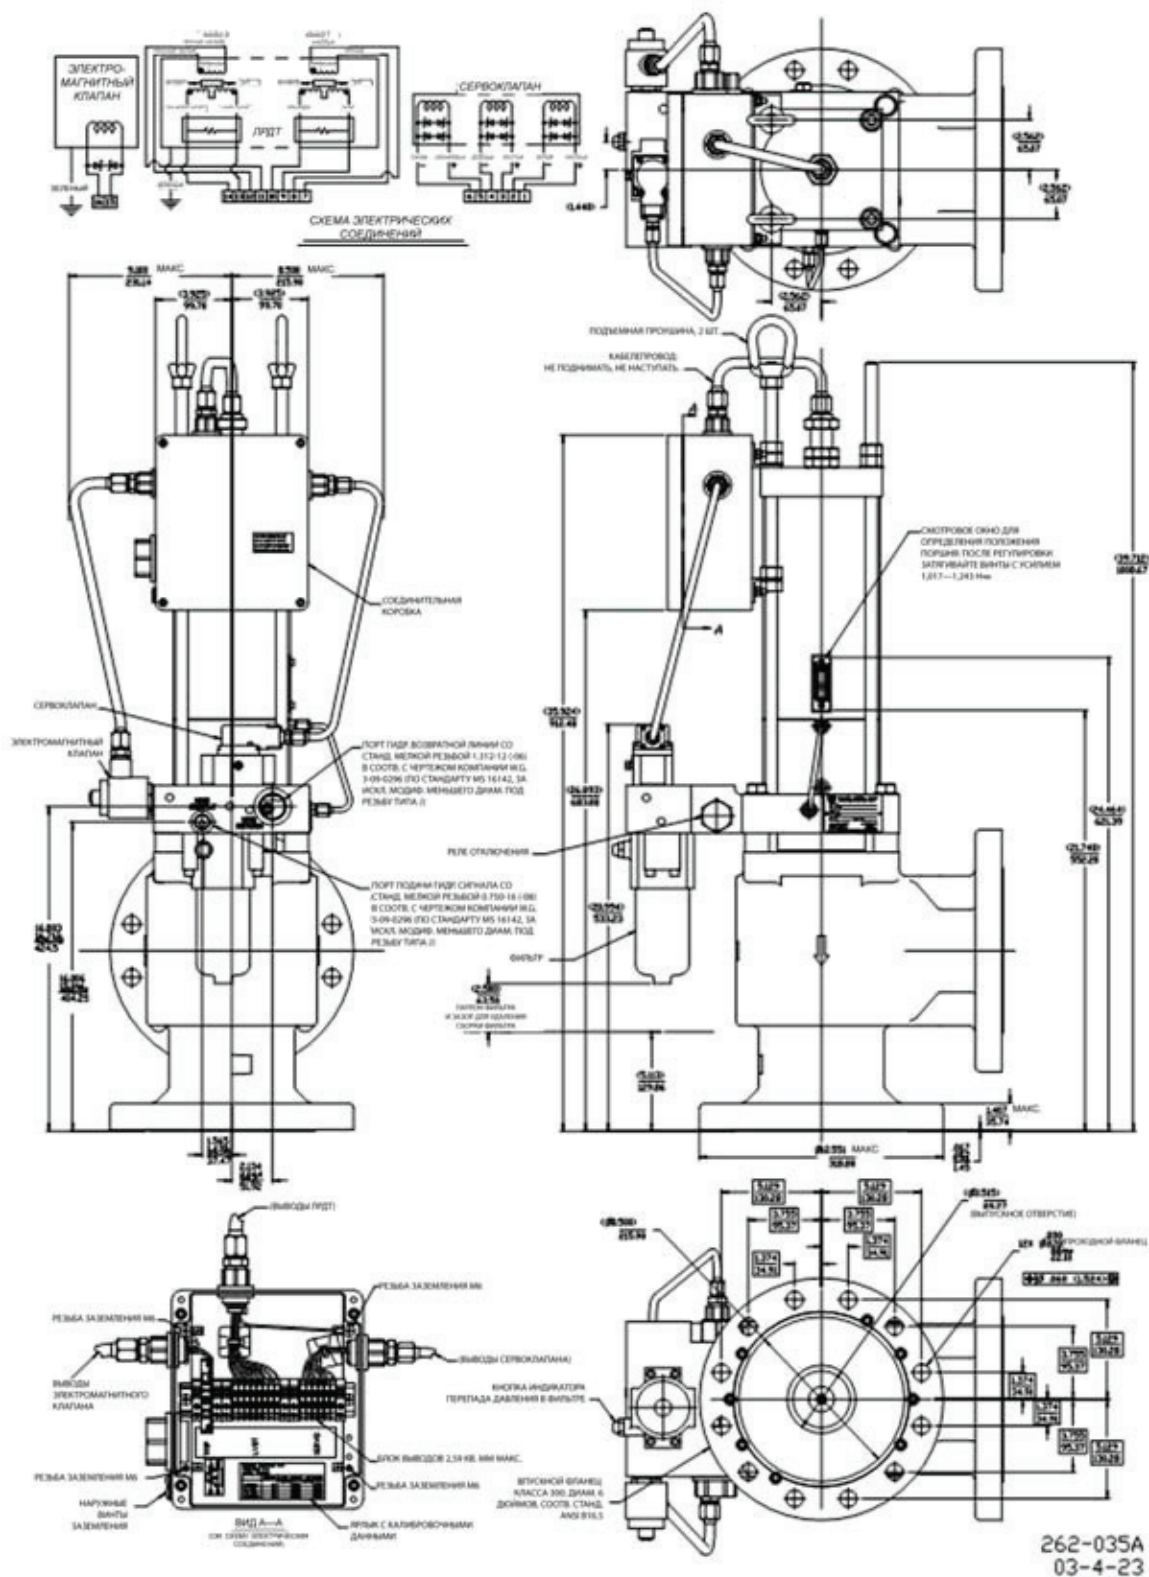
а. Контурный чертеж регулятора (6 дюймов, однофазная соединительная коробка)
